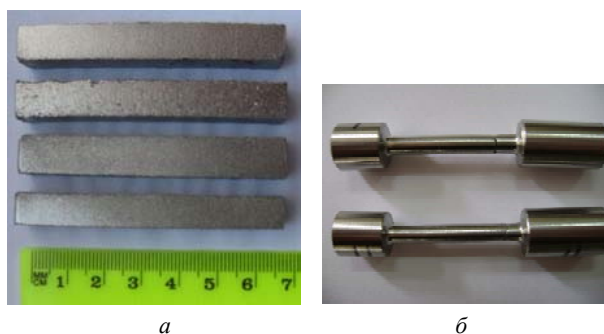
Спеченные заготовки (а) и общий вид образца (б) для испытаний на растяжение
